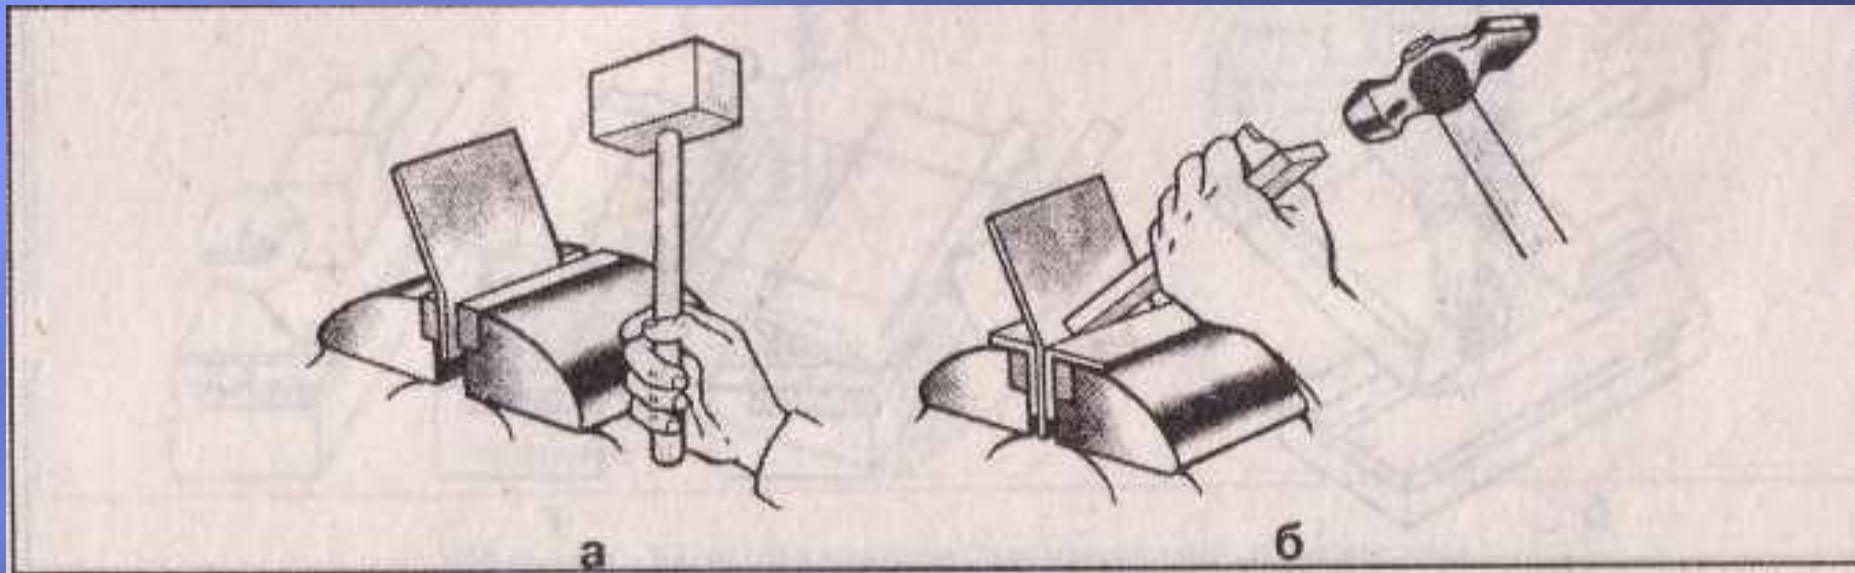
Сгибание заготовок из тонколистового металла в тисках:
